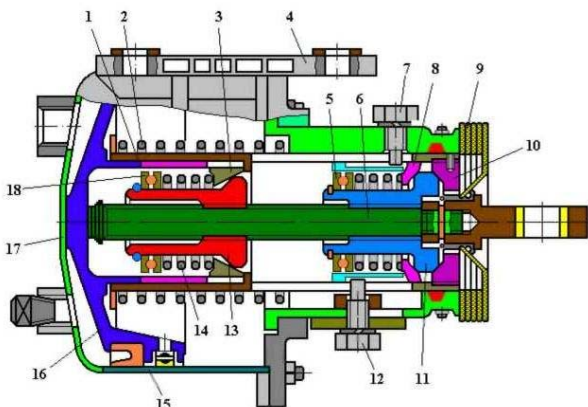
Тормозной цилиндр ТЦР-3.
